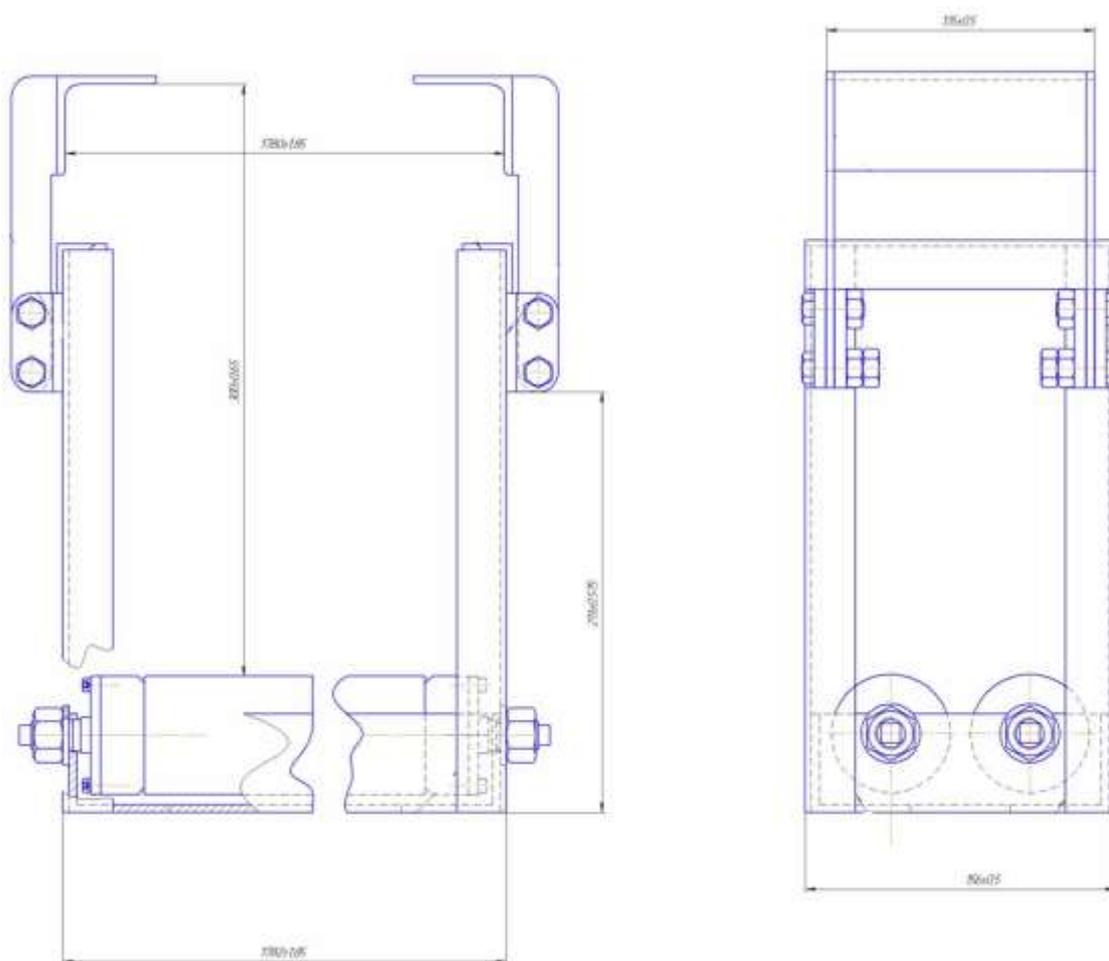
Поддерживатель изделий металлопроката к токарно-винторезному станку
